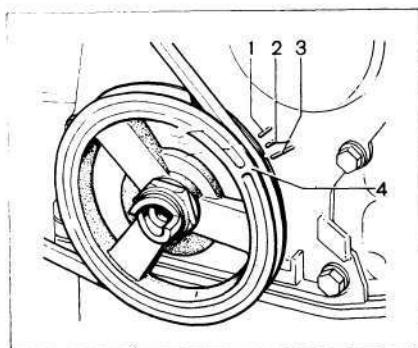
Метки на шкиве и крышке привода механизма газораспределения: 1—10°; 2—5°; 3—0° (ВМТ); 4 — метка на шкиве
